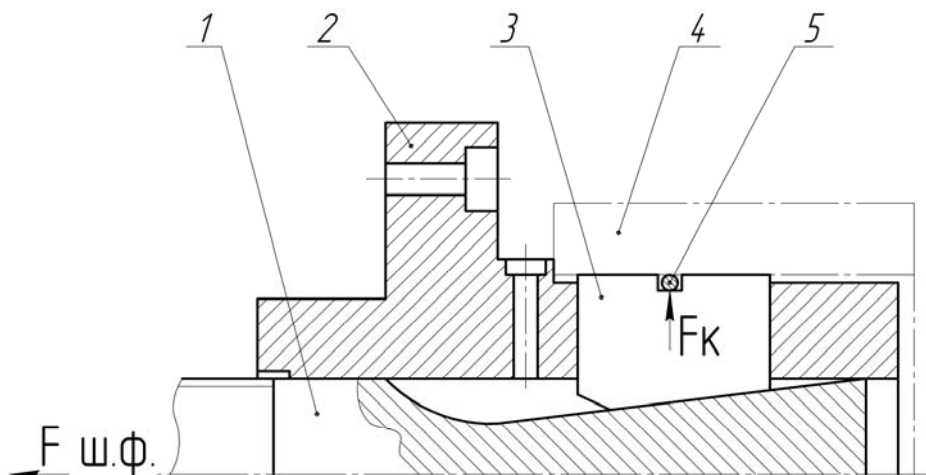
Принципиальная схема однорядной кулачковой пневматической оправки.
